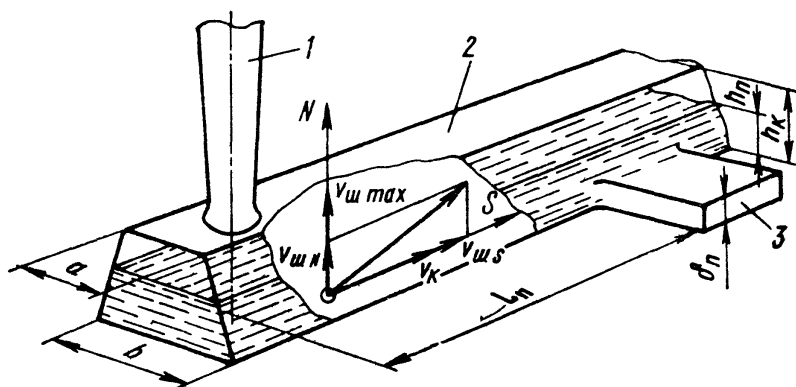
Схема установления высоты потока в коллекторе в начальный период заливки и движения шлаковой частицы в горизонтальном потоке расплава:
